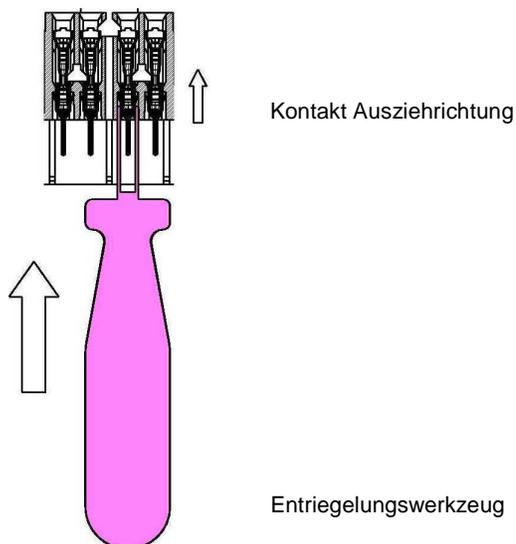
Kontakt nach vorne bis zum Anschlag vorschieben. Gleichzeitig Entriegelungswerkzeug wie abgebildet in die Kontaktkammer führen. Anschließend zieht man vorsichtig an der entsprechenden Leitung, bis der Kontakt aus der Kammer entfernt ist.
